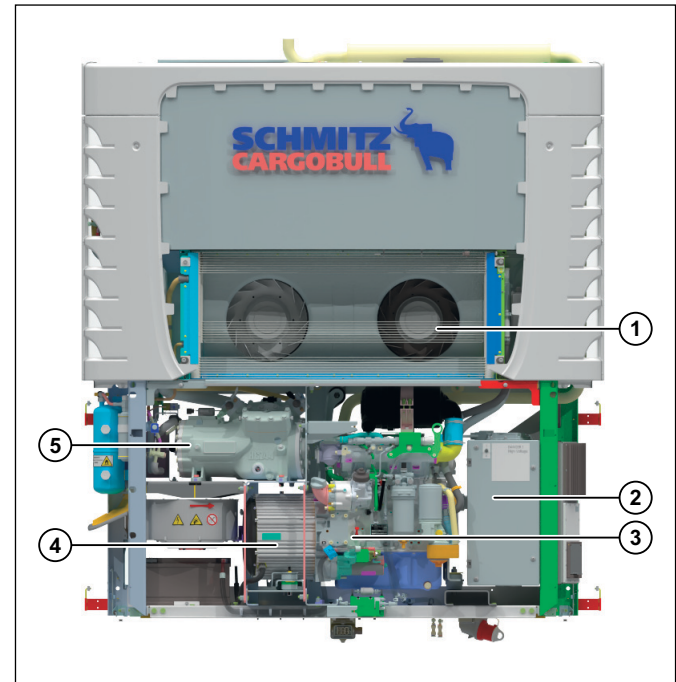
Ansicht mit geöffneten Türen (S.CU dc90)
